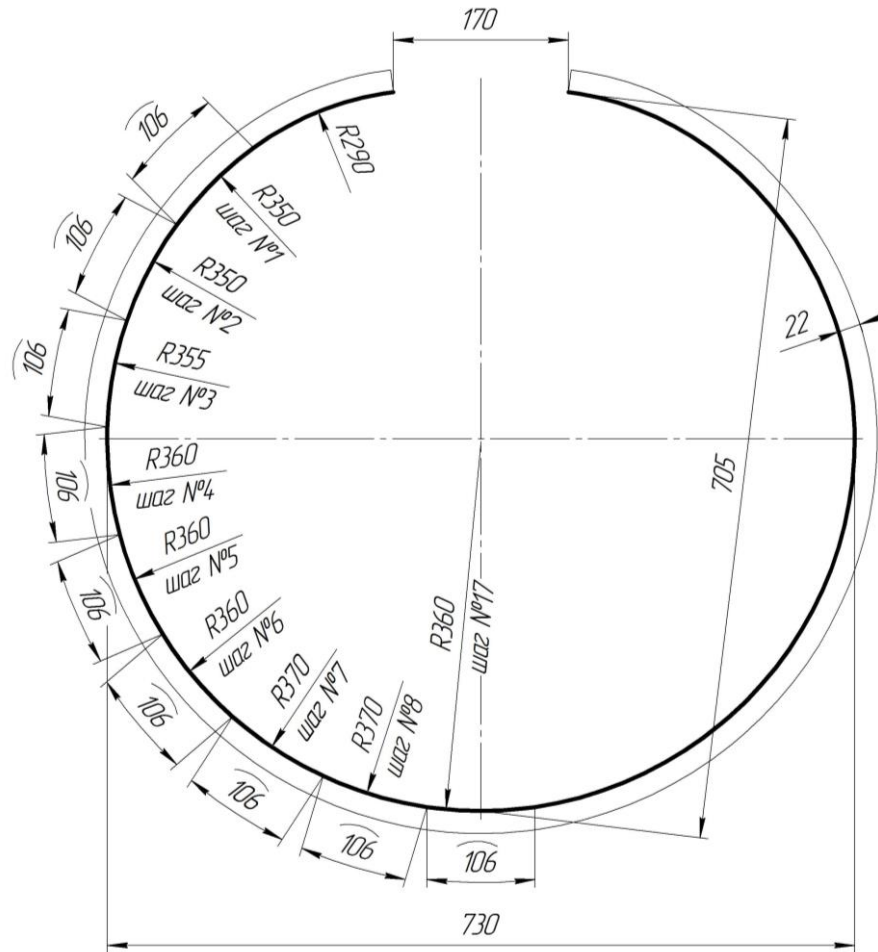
Схема профиля трубной заготовки для получения труб диаметром 720 мм с толщиной стенки 22 мм
